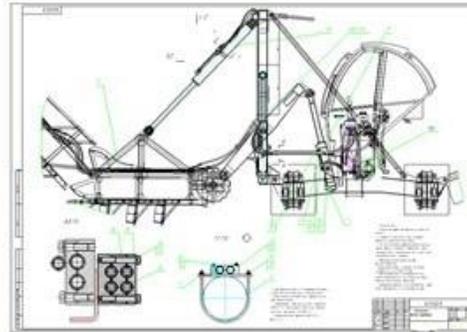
Сборочный чертеж гидросистемы вид сбоку
